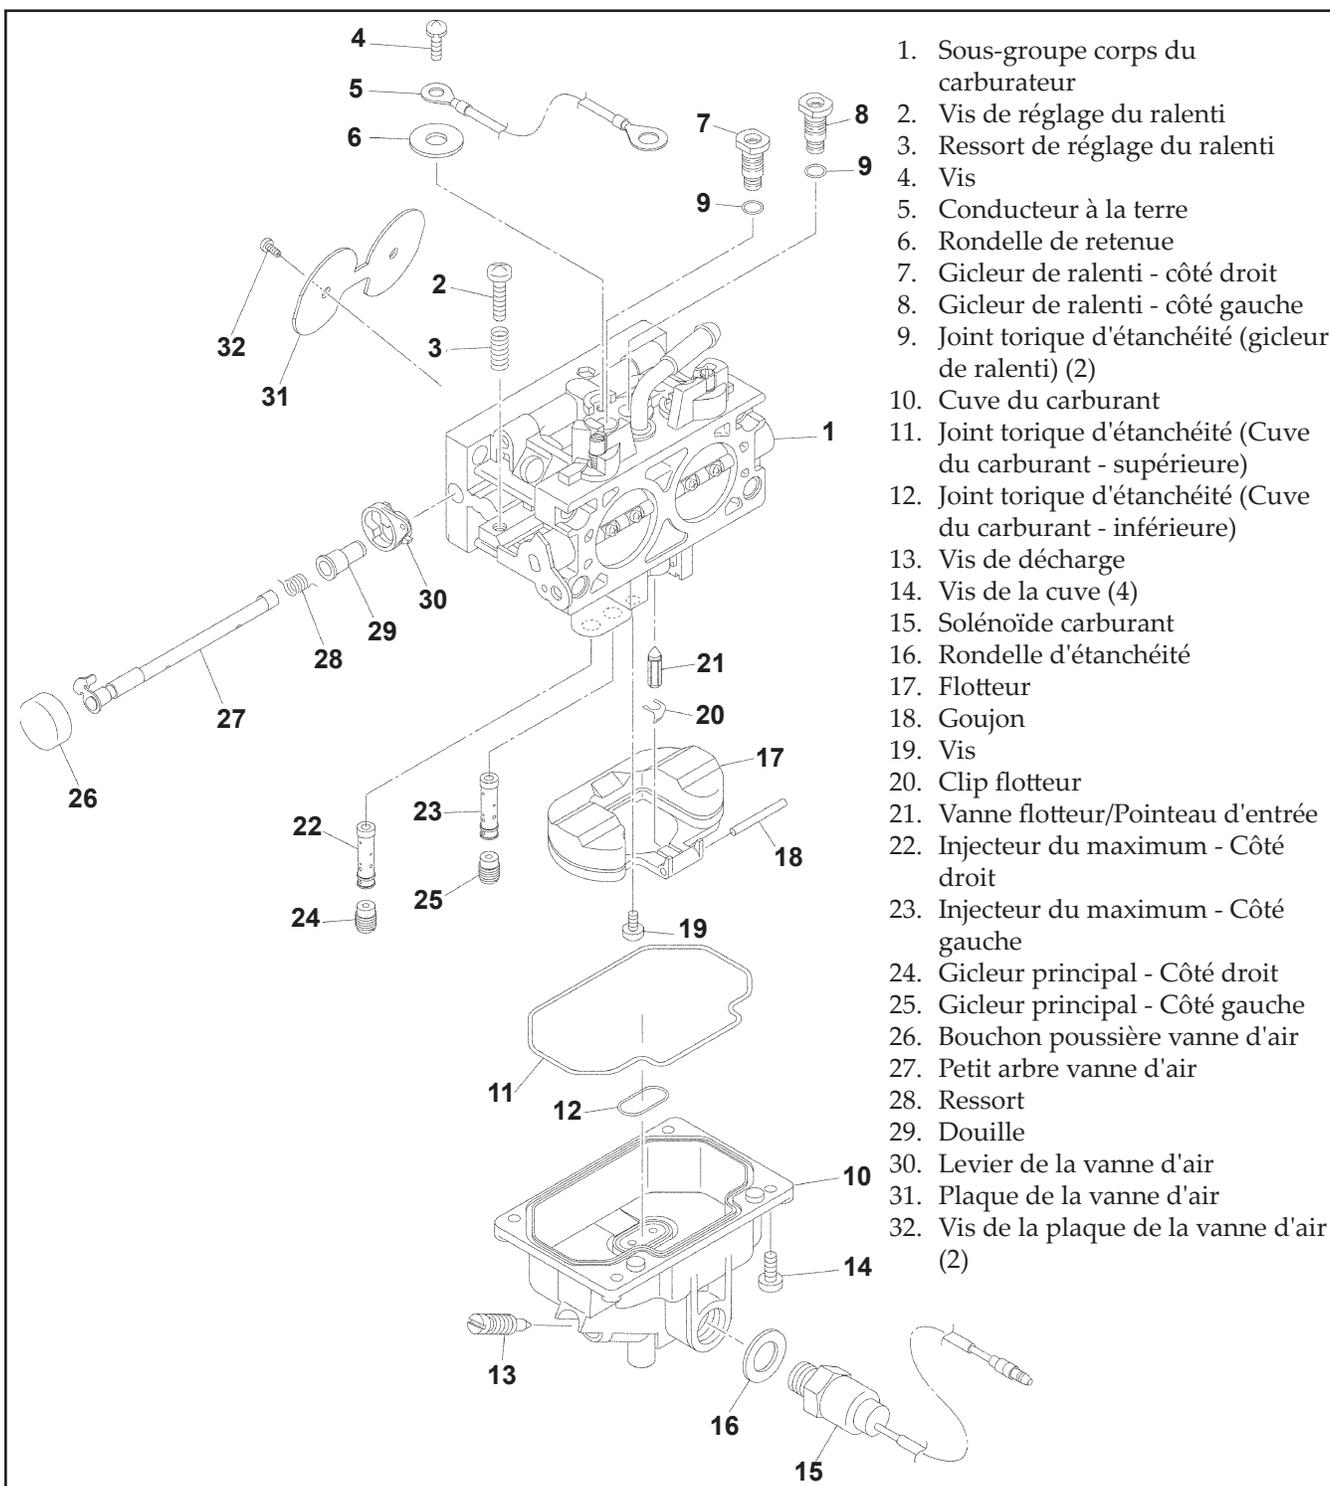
Carburateur Keihin BK bicylindre – Vue éclatée.
